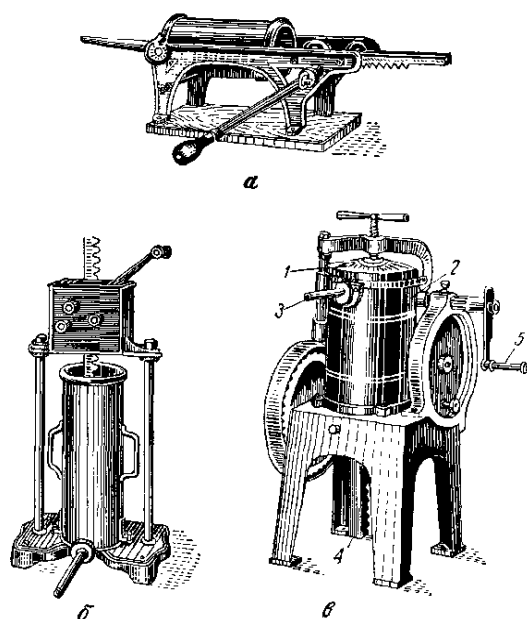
Поршневые шприцы с ручным приводом: а - с поворотным цилиндром; б - с выдвижным; в - с вертикальным цилиндром и откидной крышкой [96]
